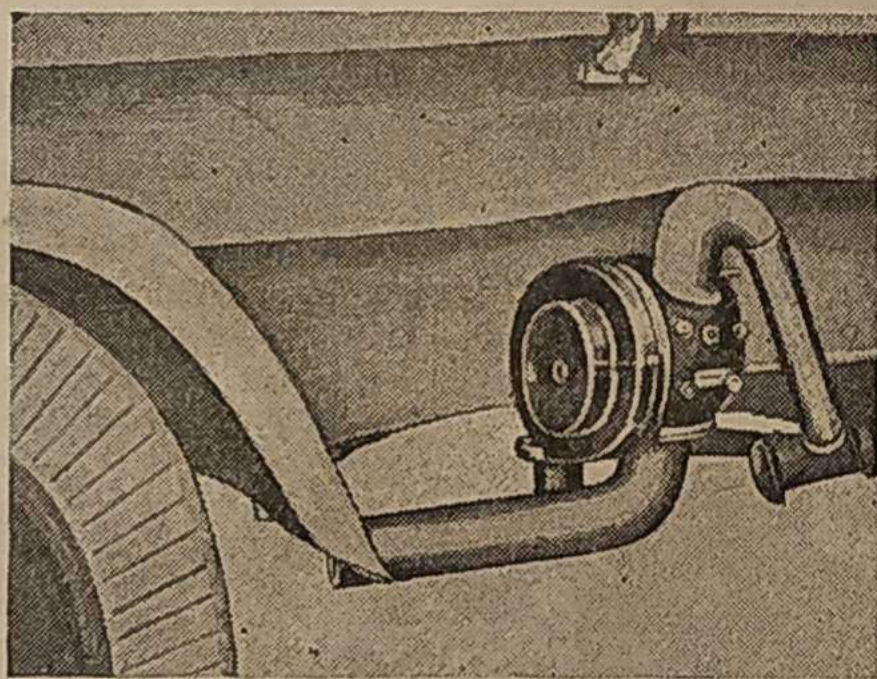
Монтаж турбокомпрессора типа „Броун-Бовери“ на шасси газогенераторного автомобиля.
